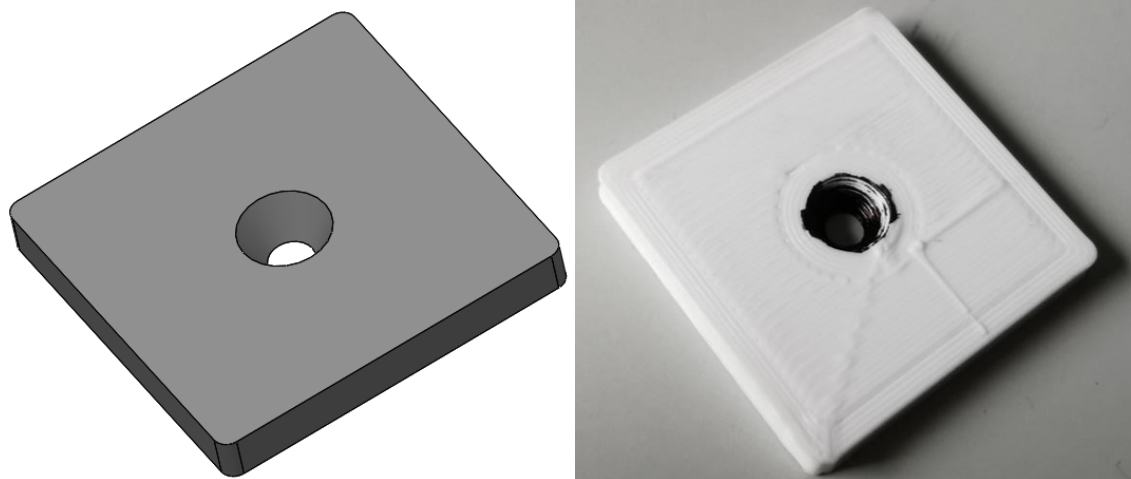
Espaçador referente à marcação do ponto de soldadura, representação em Software Solidworks (a), e após impressão 3D, (b)
